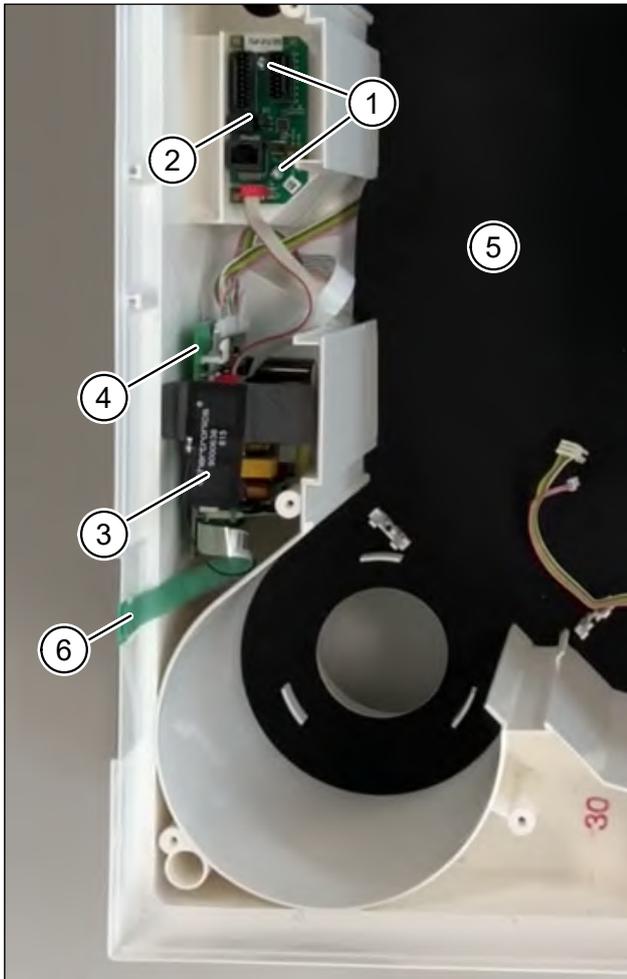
Schnittstellen- und Steuerplatine entfernen
